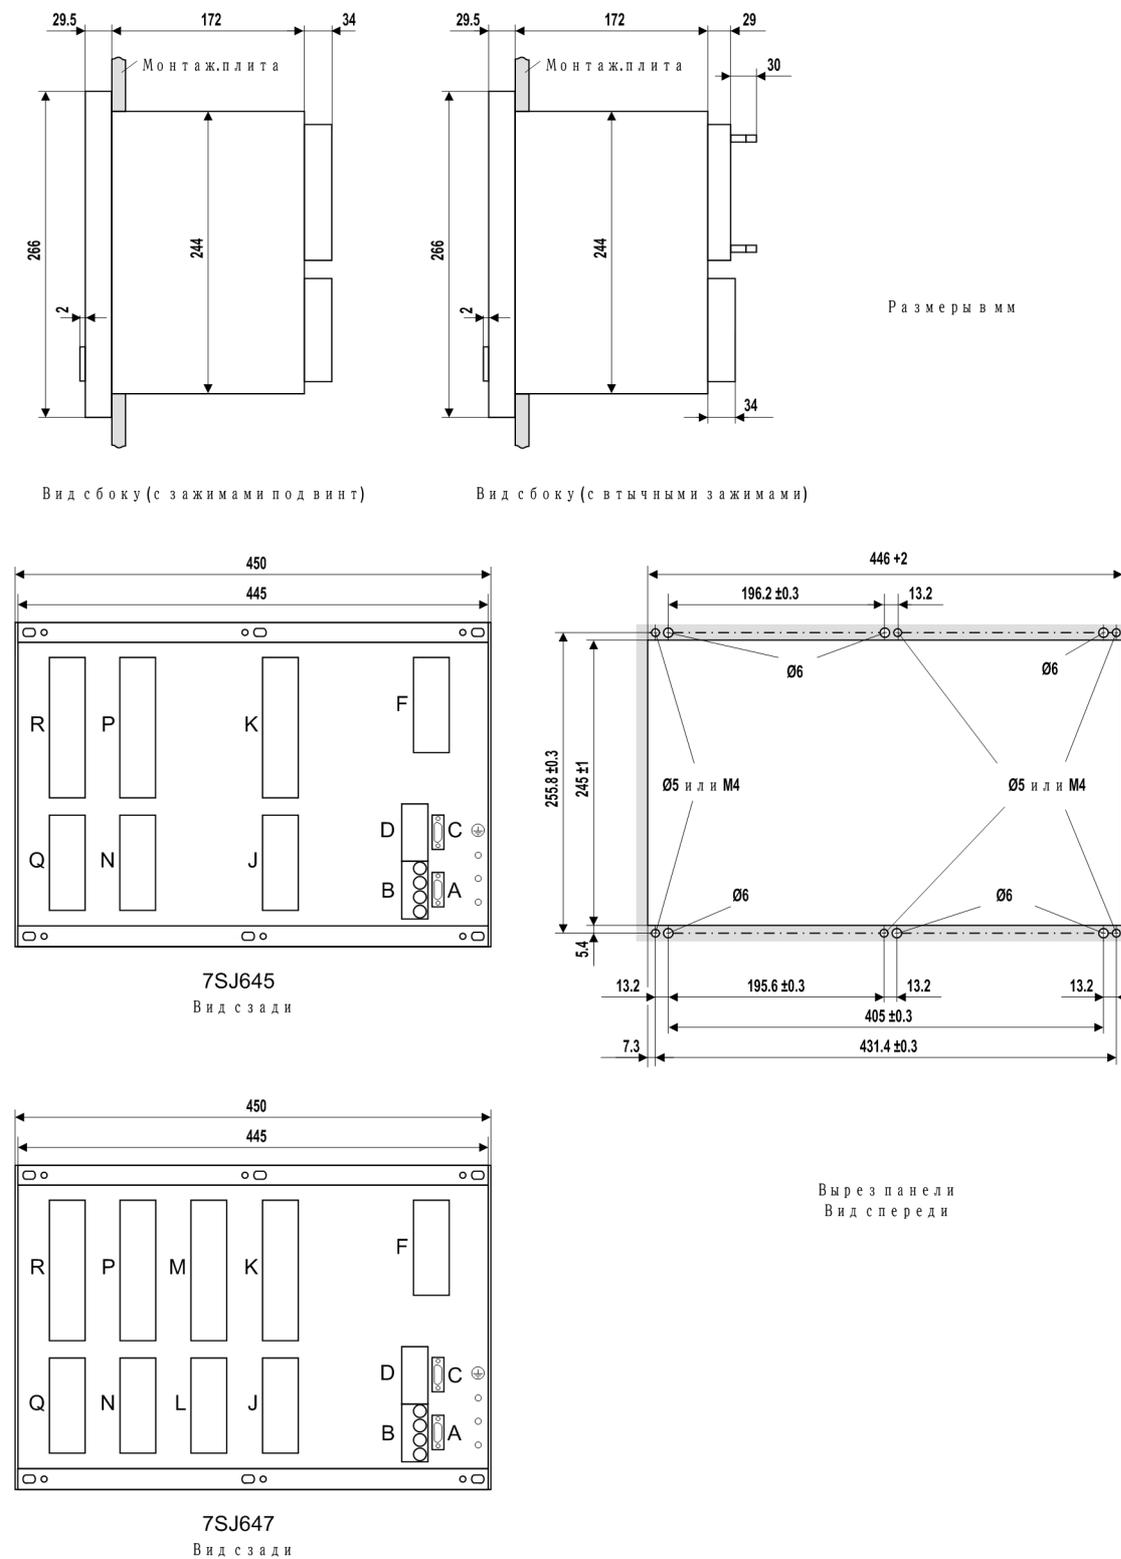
Размерный чертеж устройства 7SJ64 для утопленного монтажа на панели и в шкафу (размер корпуса 1/1)
